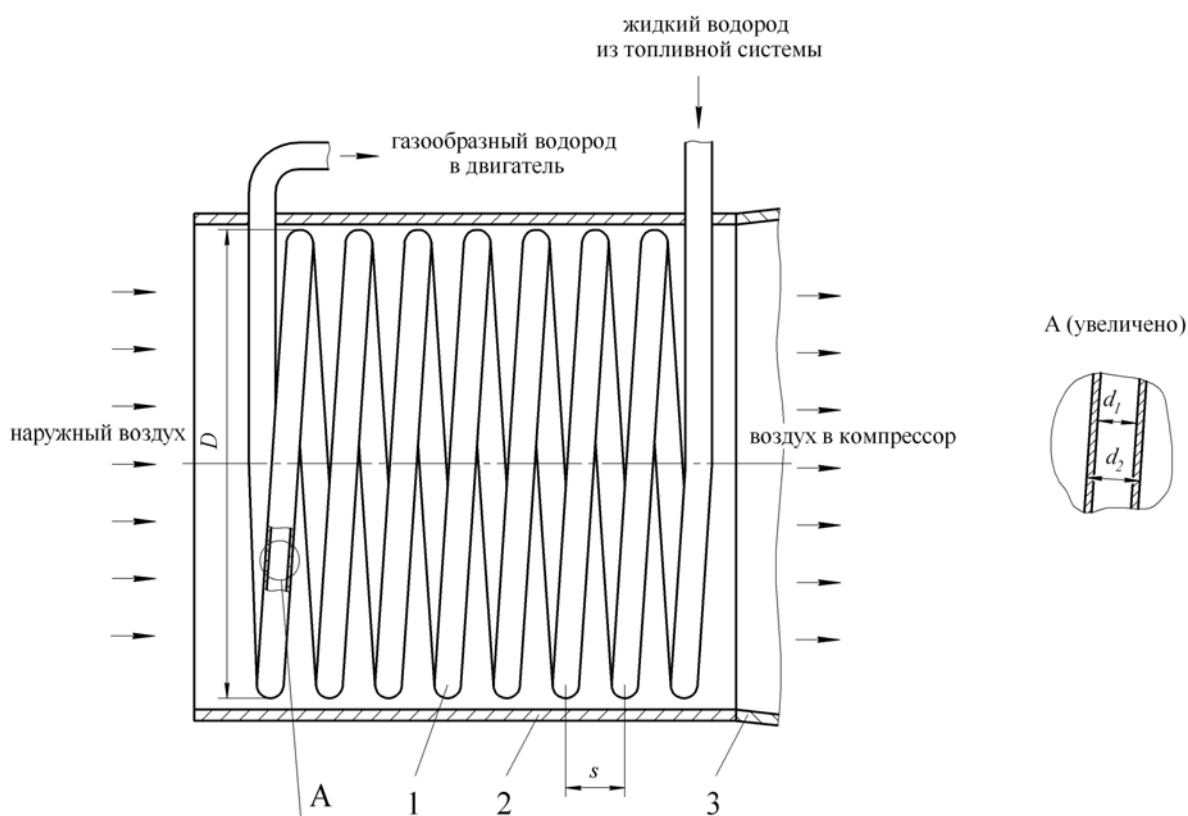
Теплообменный аппарат витой конструкции для охлаждения воздуха перед компрессором:
